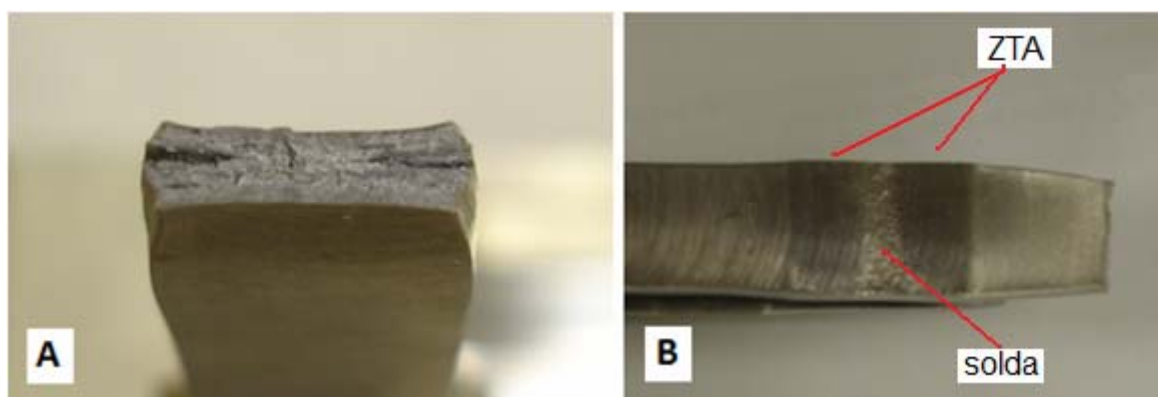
Detalhes do corpo de prova do aço S41030 com junta soldada após ruptura sob tração.
